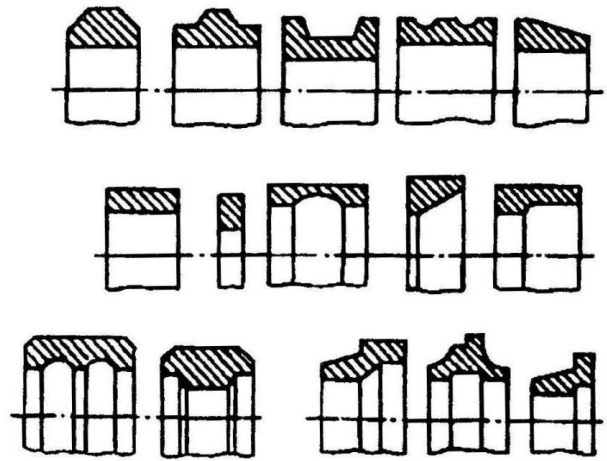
Форми перетинів кільцевих заготовок, виготовлених розкатуванням
